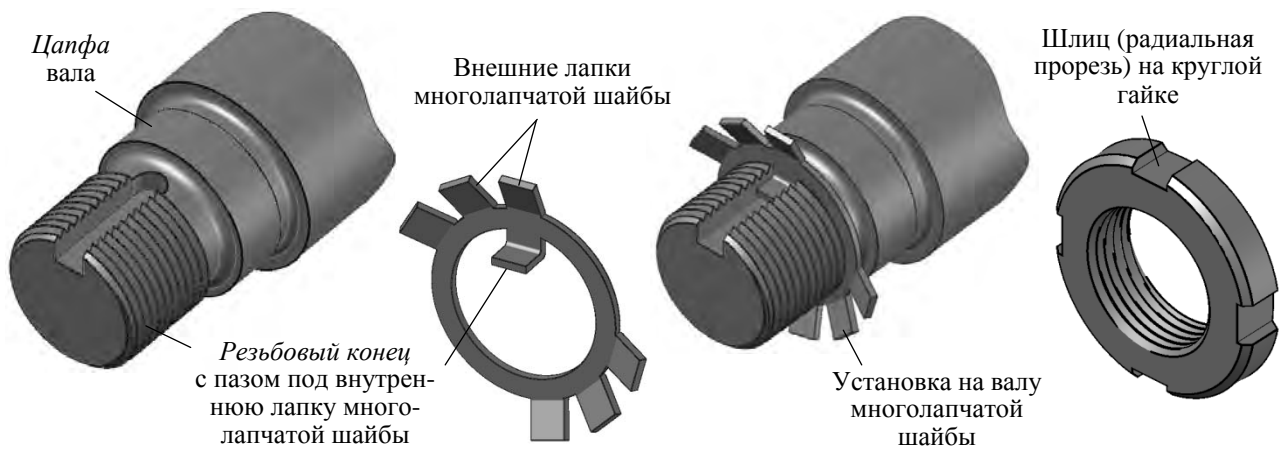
Резьбовые элементы для крепления на цапфе вала насаживаемых деталей гайкой
